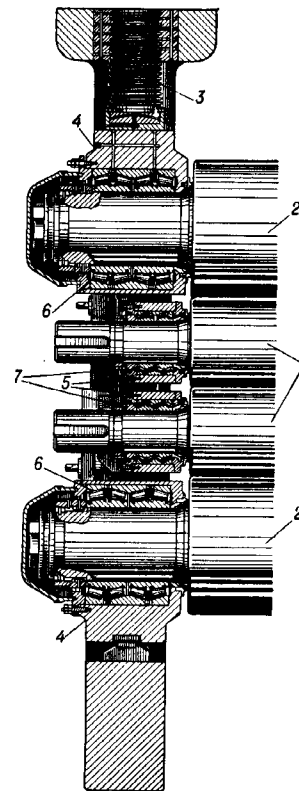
Роликовые подшипники с подушками к листовому четырёхвалковому прокатному стану: 1 — прокатные рабочие валки; 2 — опорные валки; 3 — нажимной винт; 4 — подушки опорных валков; 5 — подушки рабочих валков; 6 — роликовые подшипники опорных валков; 7 — роликовые подшипники рабочих валков.
